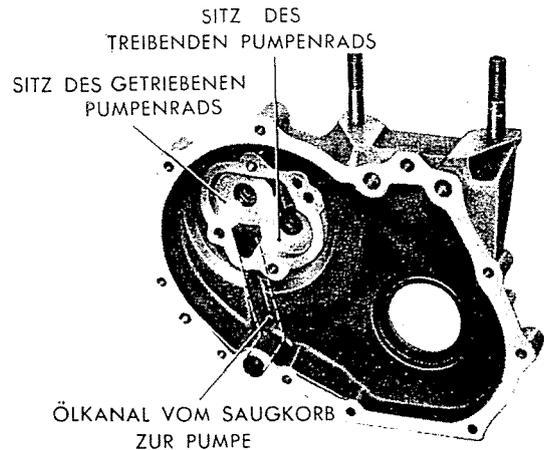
Steuergehäusedeckel mit Ölpumpensitz.
